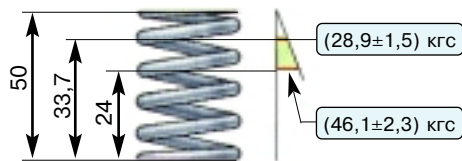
Основные данные для проверки наружной пружины клапана двигателя мод. 2106-70
